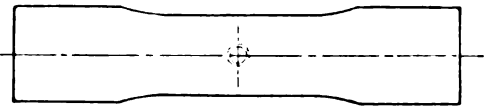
C. Stäbe mit Gewindelöchern M 10.
